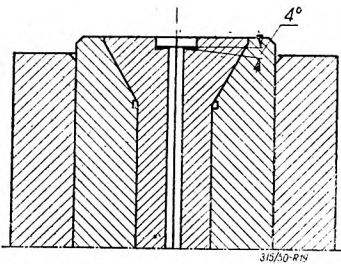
Plan obróbki przekładek dla łopatek typu 2.
